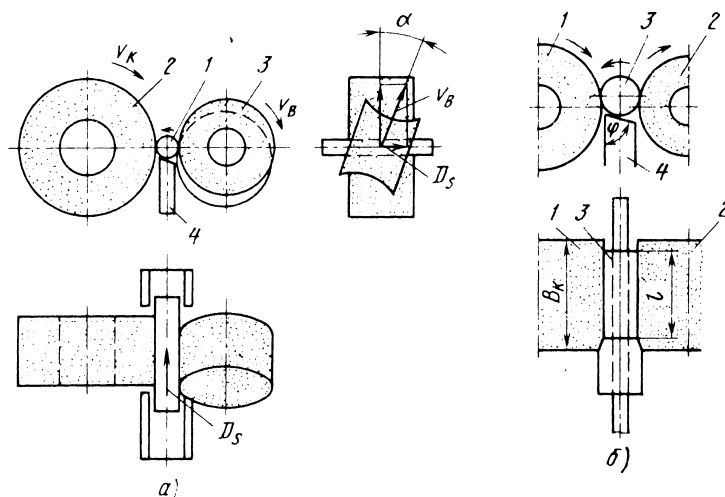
Схема бесцентрового круглого шлифования: а) проходного, б) врезного
